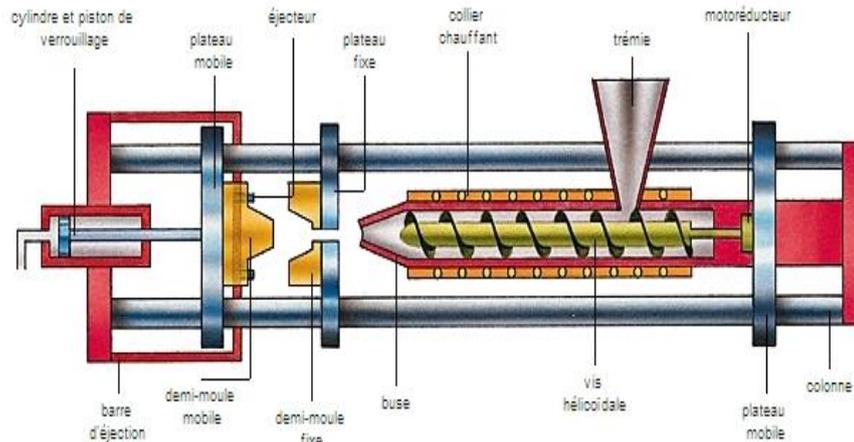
3: Le schéma d'une machine de moulage par injection.⁷
